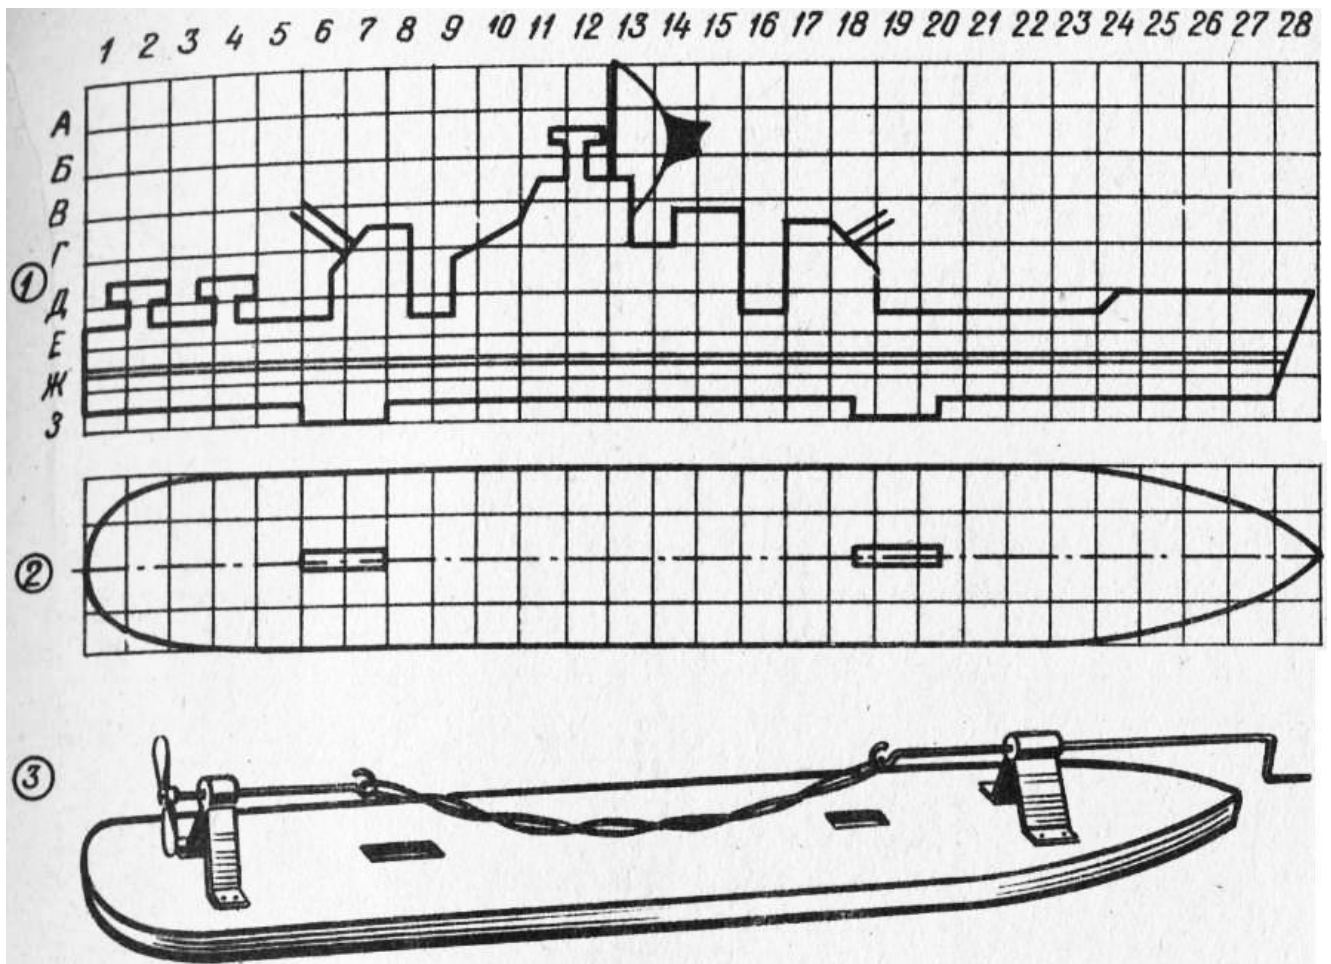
Модель корабля противолодочной обороны: 1 — силуэт корабля; 2 — вид сверху на днище корпуса; 3 — наглядное изображение установки резинодвигателя
